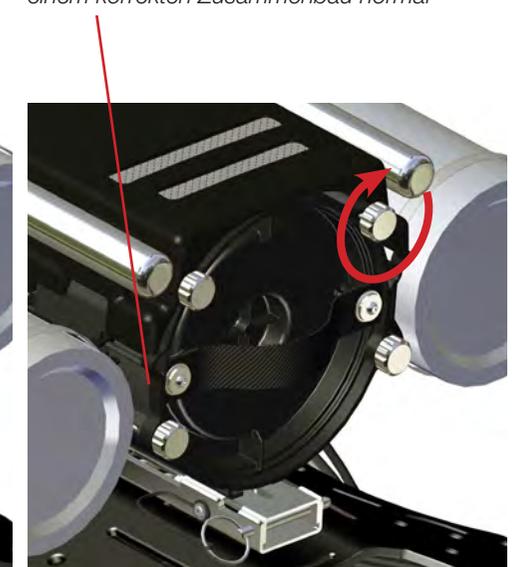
Ziehen Sie die vier Schrauben an.
